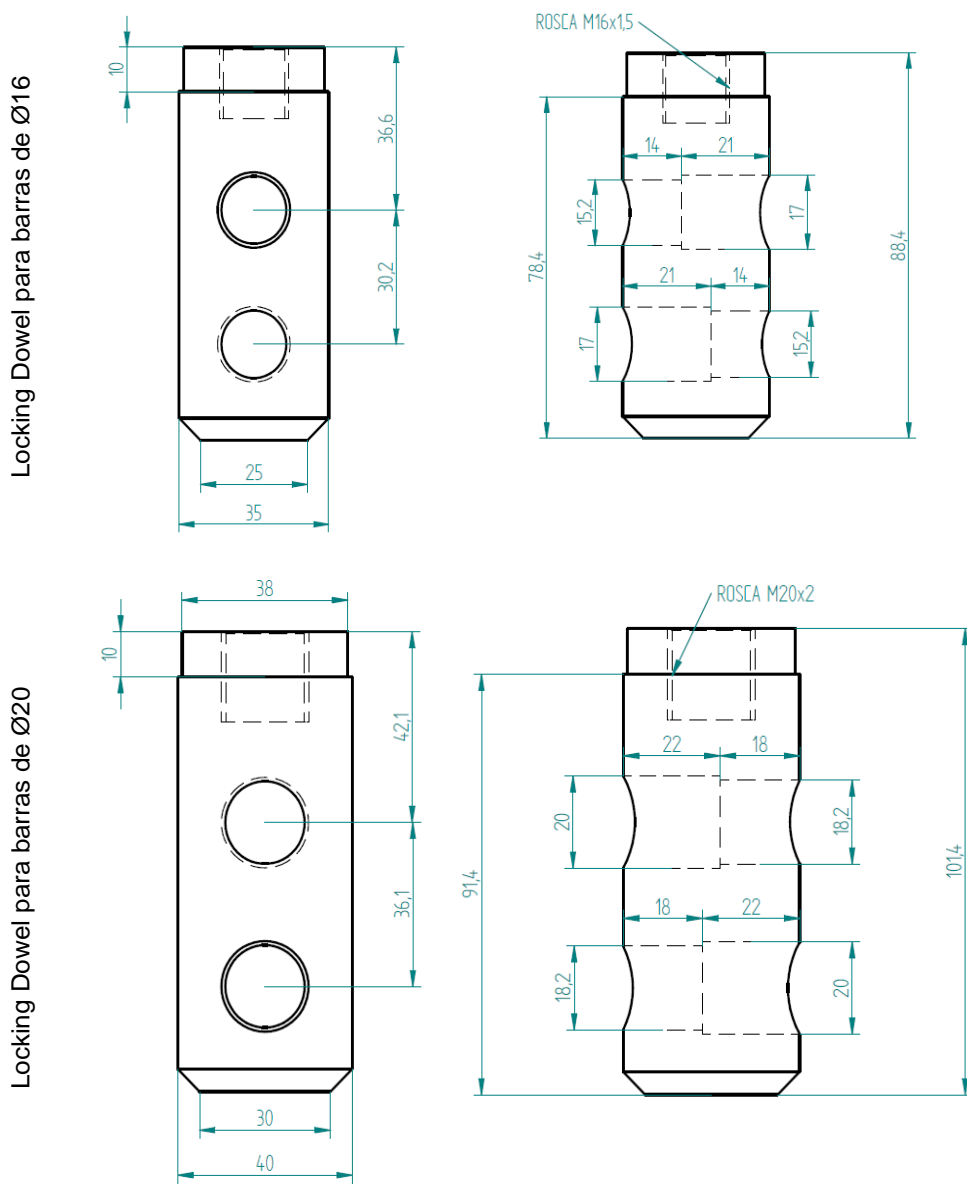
Dimensiones del Locking Dowel (unidades en mm)
